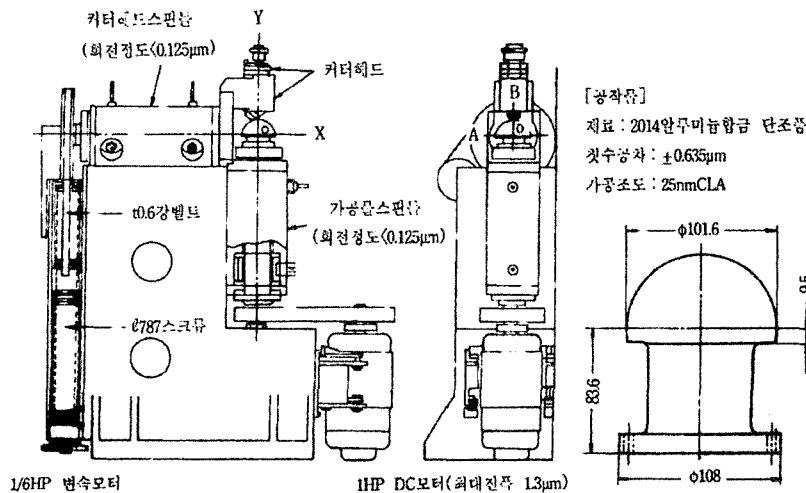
du Pont 1호기(Hemisphere Turning Machine)의 구조
